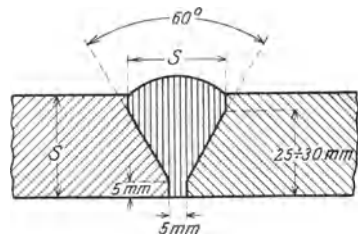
Bearbeitung der Schweißmulde ohne Stiftsetzung.
